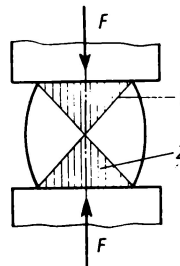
Verformungsmechanismus bei zylindrischen Druckproben. 1 Rutschfuge; 2 Druckkegel
